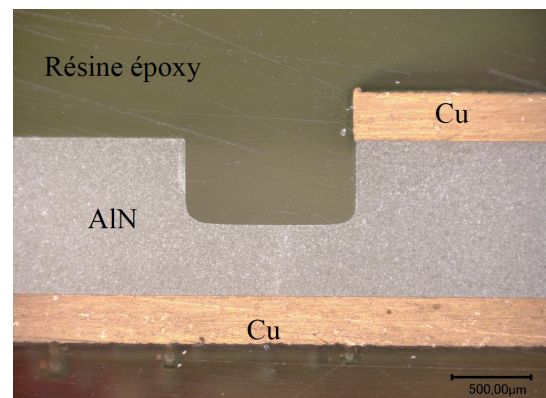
Vue en coupe du profil de la mesa par usinage ultrason.
